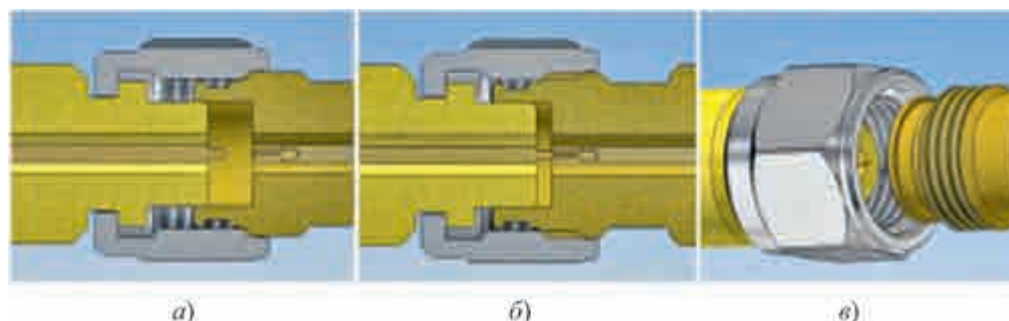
Схема соединения вилки и розетки соединителя 1,35 мм:
